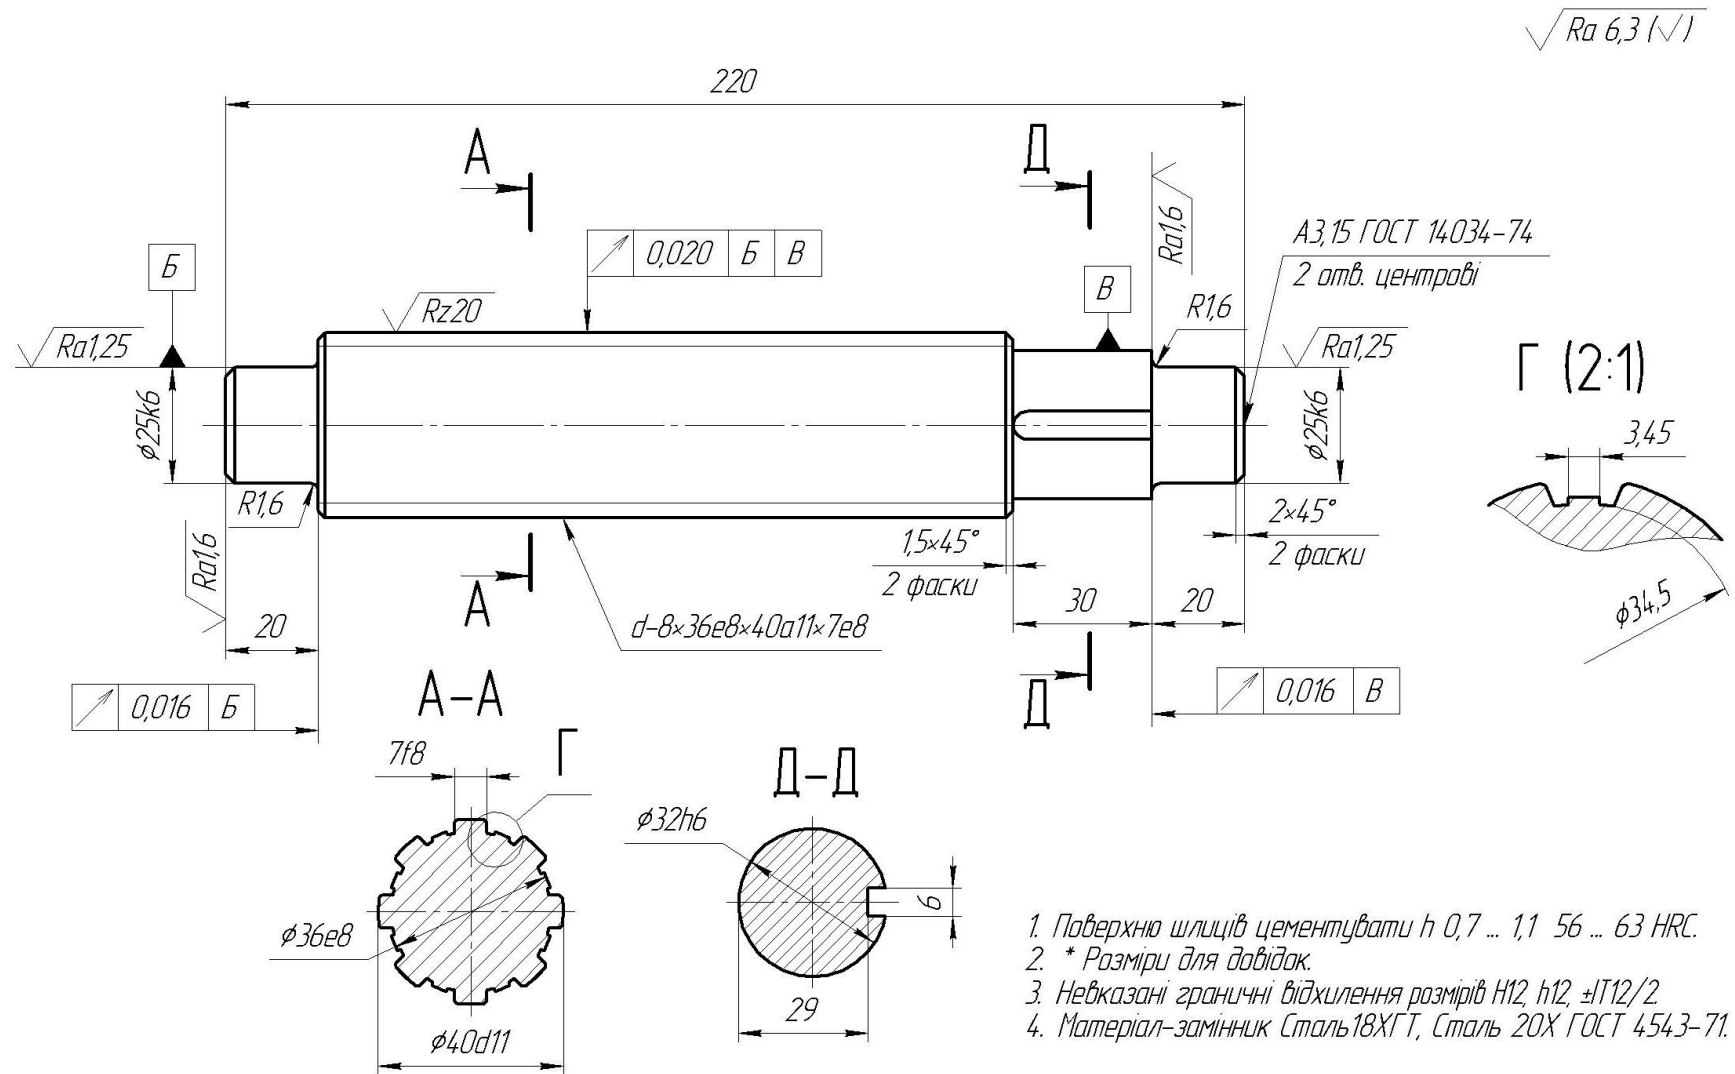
Кресленник деталі «Вал шліцьовий»
